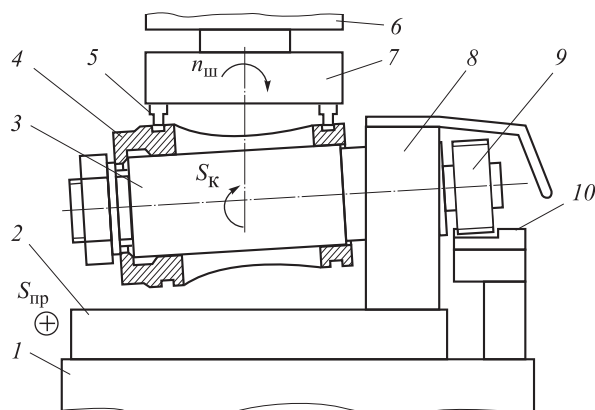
Схема модернизации вертикально-фрезерного станка для нарезания канавки
